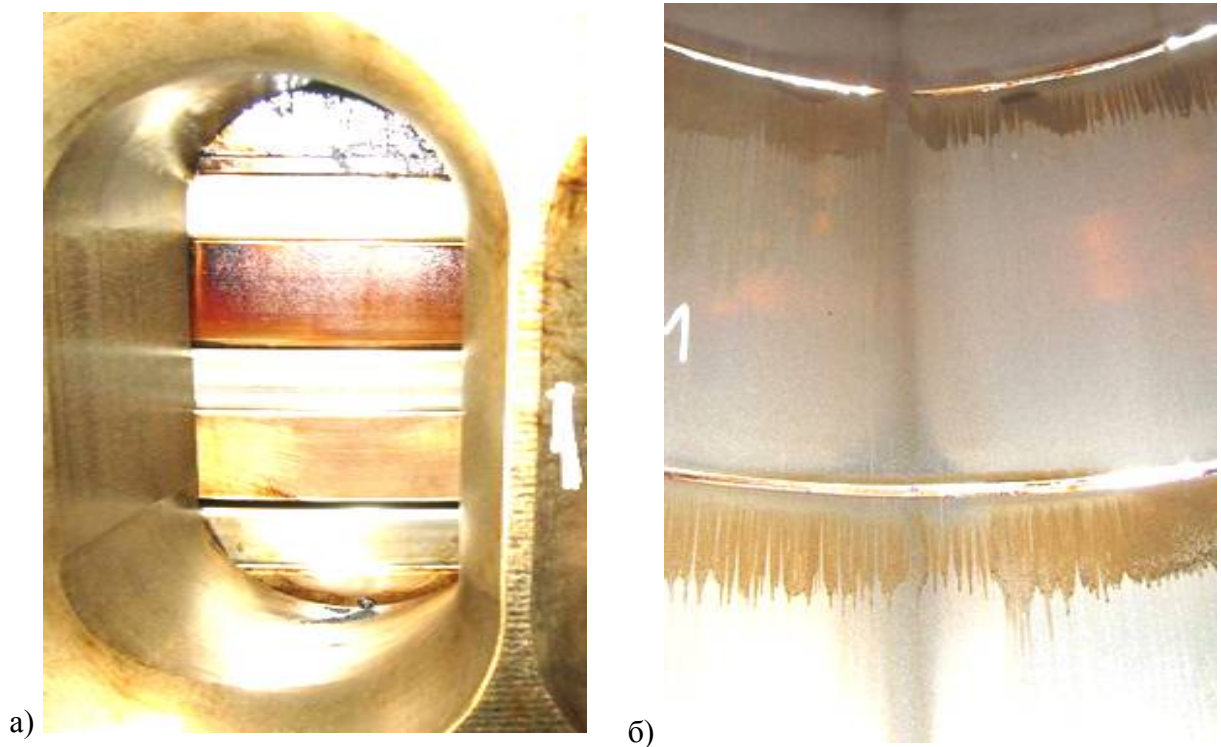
Вихідний стан деталей ЦПГ базового циліндра № 1:
